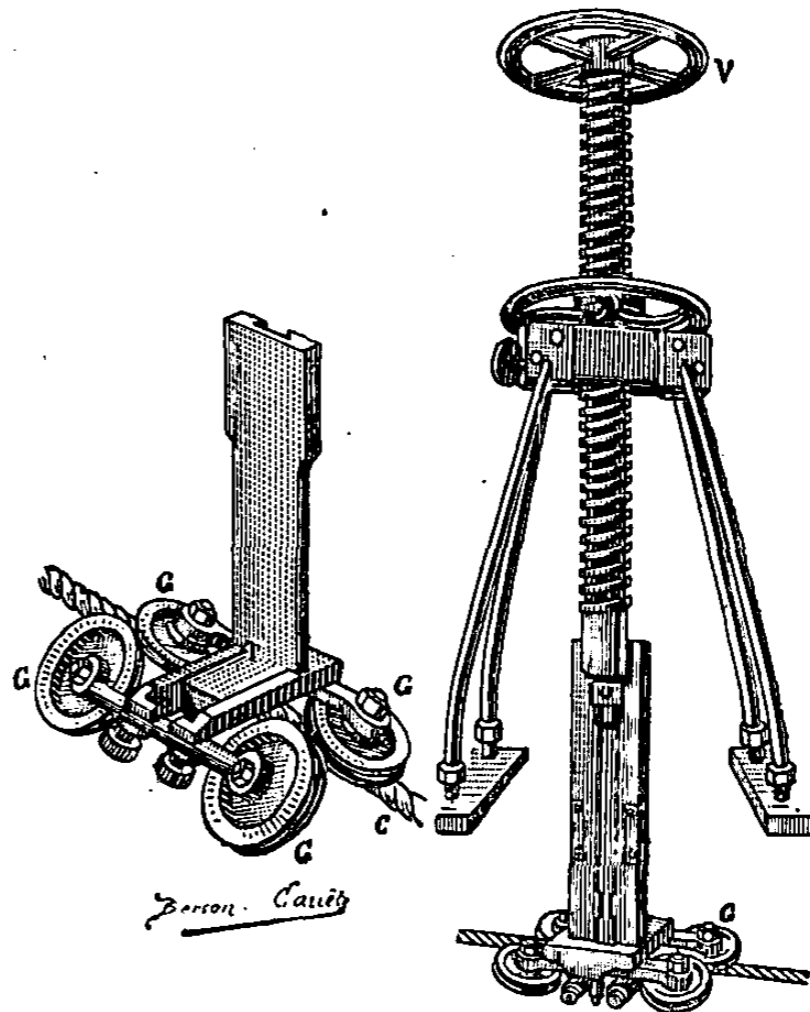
et 374. — Machine des tramways de San-Francisco. Vue des galets qui saisissent le câble. Vue d'ensemble.
